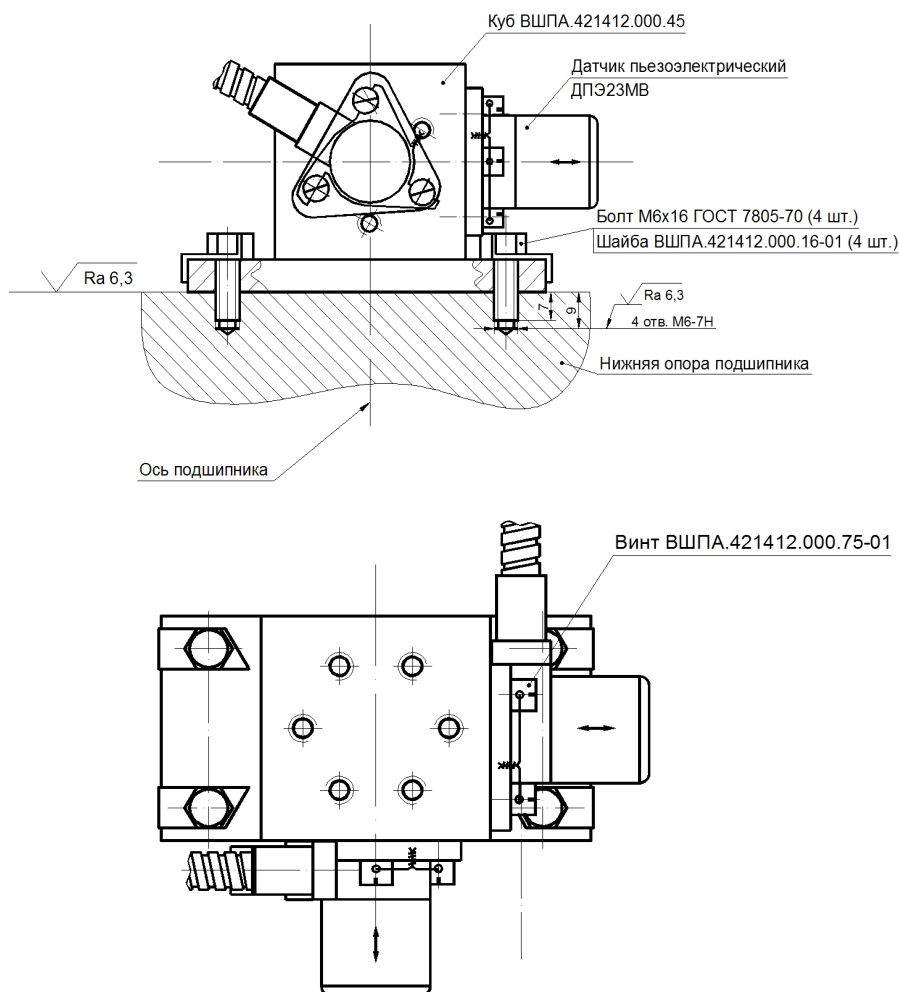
Установка датчика пьезоэлектрического на опоре подшипника
